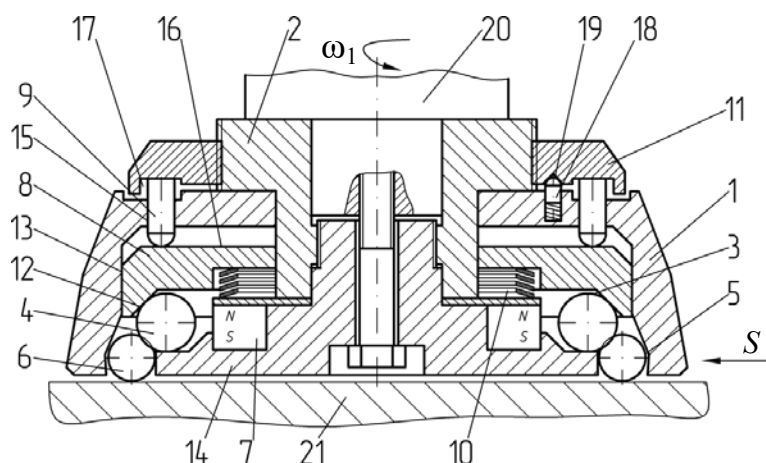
Инструмент для МДН плоских поверхностей с устройством регулирования натяга между деформирующими и приводными шарами
